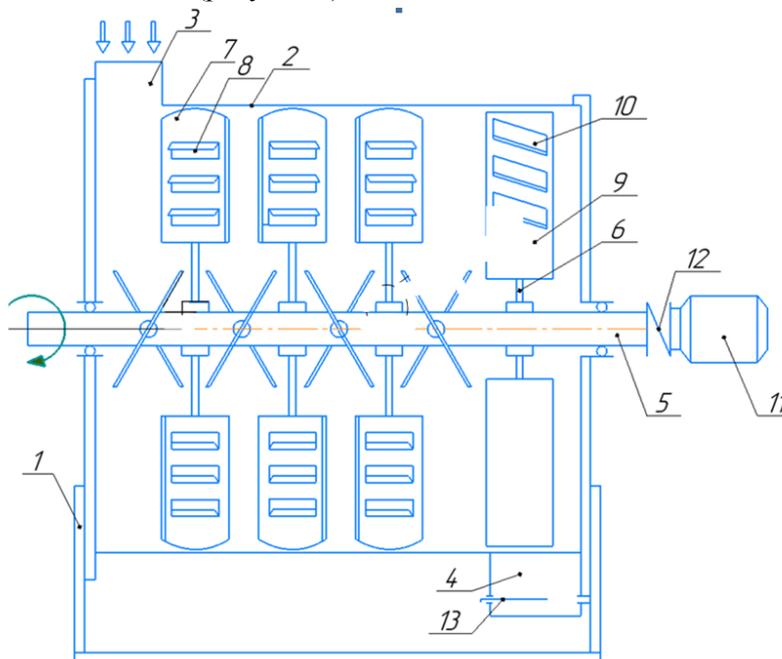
Схема лопастного смесителя: 1 - рама; 2 - цилиндрический корпус;
